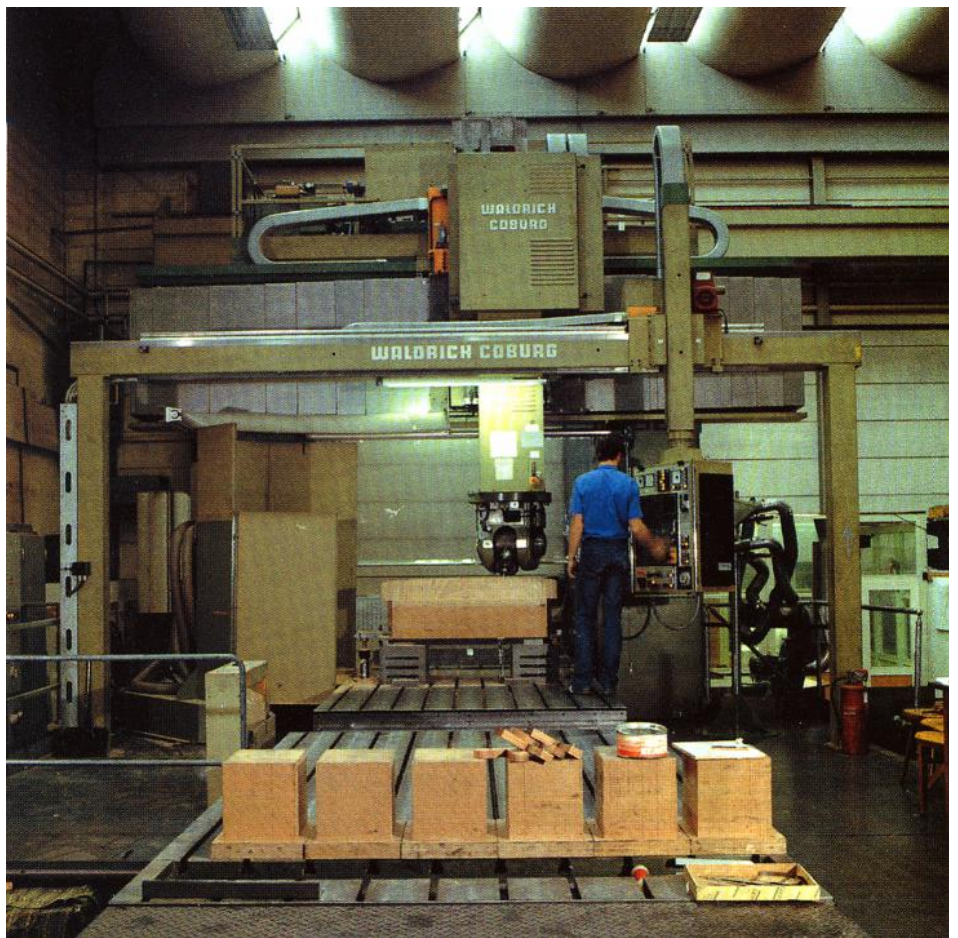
CMC gesteuerte, 5-achsige Bearbeitungsmaschine Fa. Waldrich-Coburg; Steuerung ATEC
